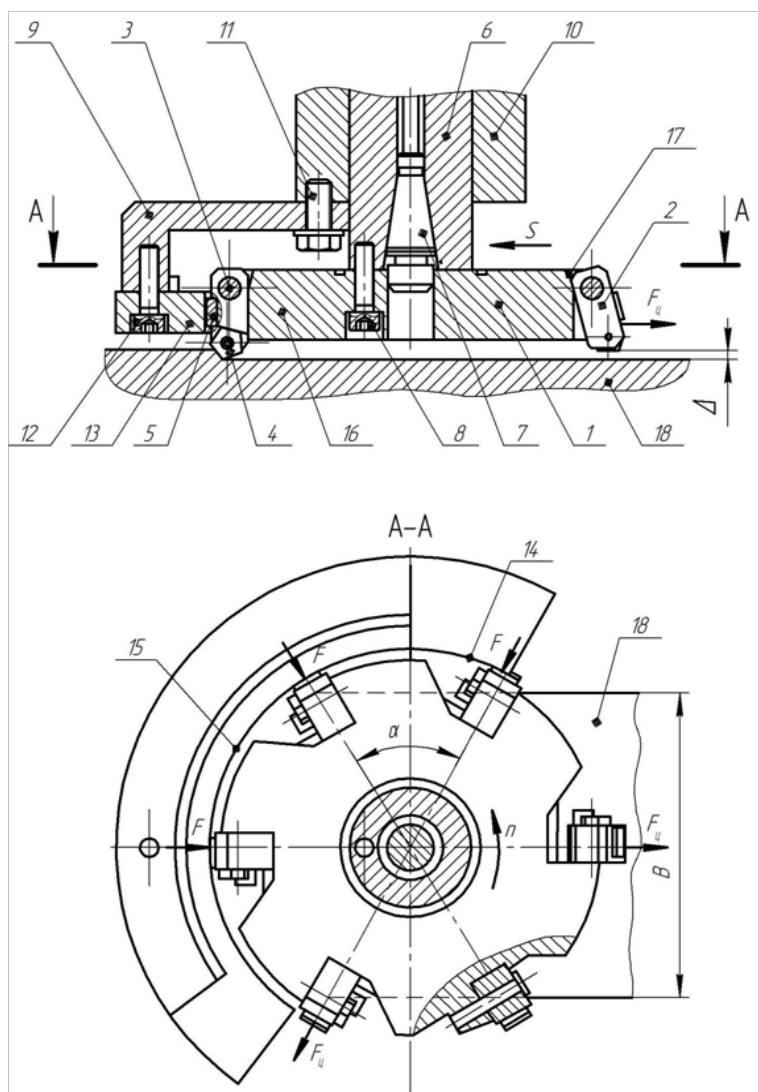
Конструкция торцевой фрезы с поворотными ножами
